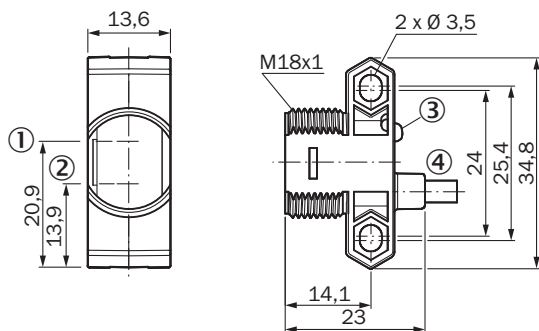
ZLx18-1xxxxx/ZLx18-Axxxxx, Leitung
